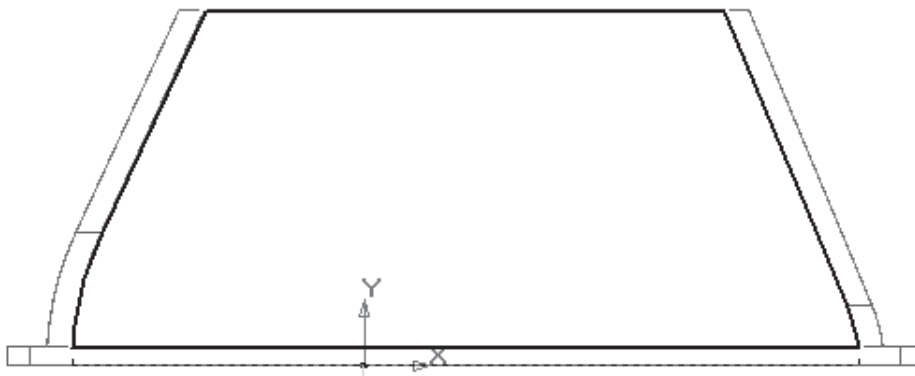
Ескіз для витискування бічної стінки корпусу редуктора
